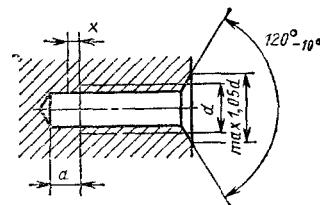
Форма сбега и недореза для внутренней метрической резьбы
